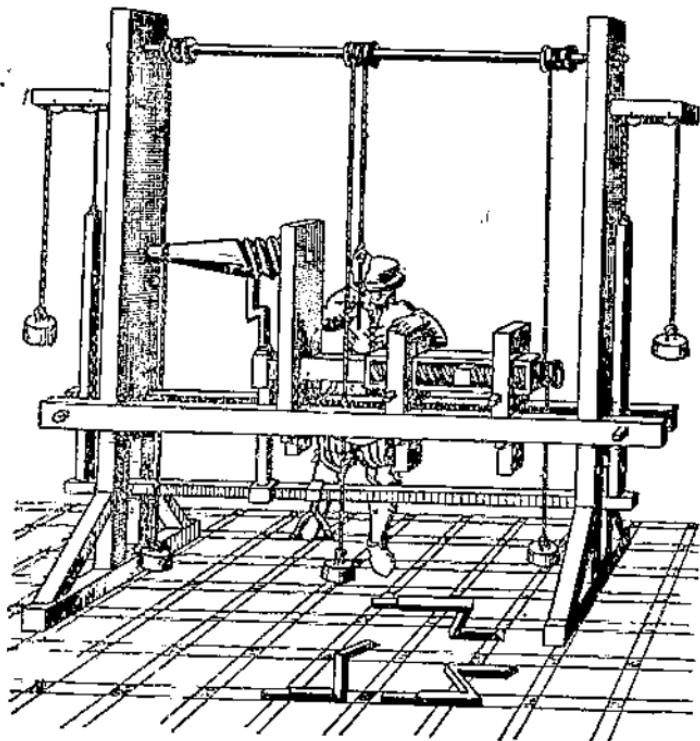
Токарный станок Бессона с механической подачей резца (конец XVI в.).
